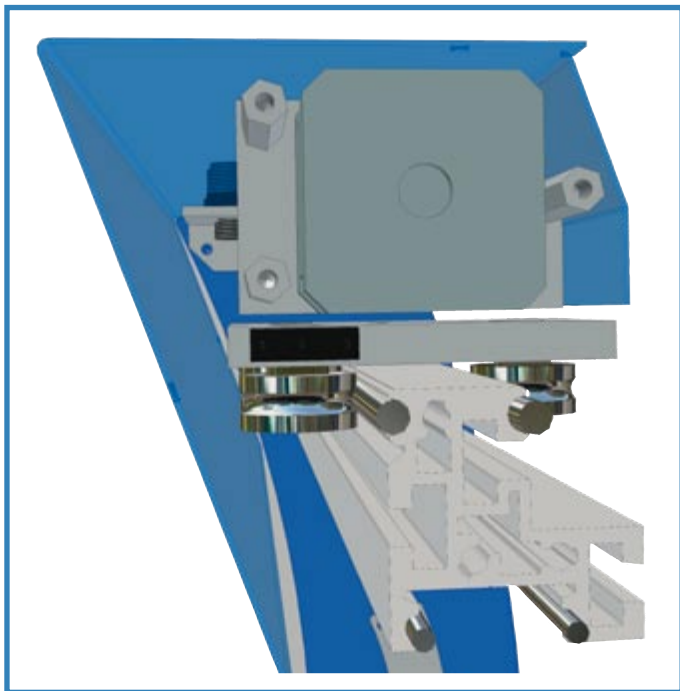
Dibujo de la sección de corte del cabezal montado en el puente.
